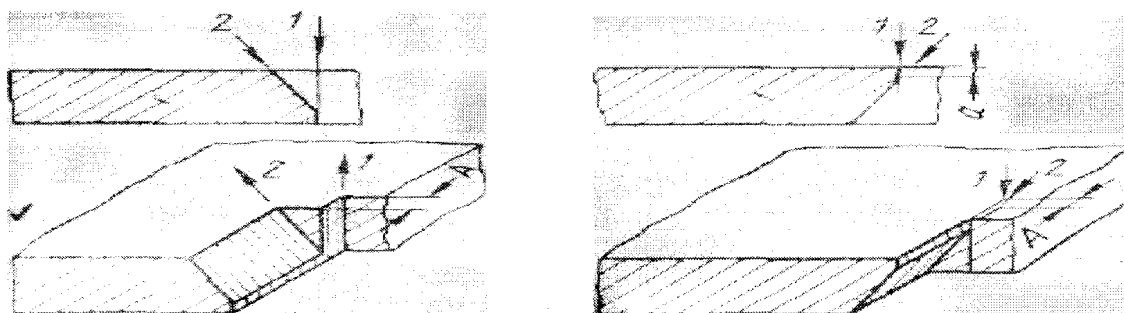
Схема резки двумя резаками со скосом кромок под сварку: а—обычная схема; б—перевернутая схема
